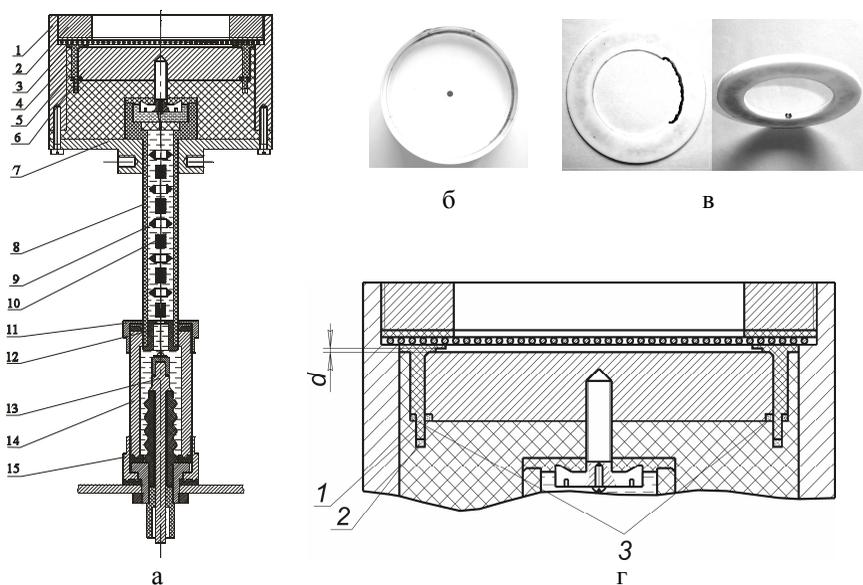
Схема конструкции: а - газоразрядного прибора (1 - корпус; 2 - анодное кольцо; 3 - анод-сетка с медным кольцом; 4 - изолятор катода; 5 - фторопластовая прокладка; 6 - катод; 7 - крышка корпуса; 8 - фторопластовая оболочка; 9 - стабилизирующие диски; 10 - трубочки; 11 – верхняя крышка высоковольтного ввода; 12 – фторопластовый стакан; 13 - керамический ввод; 14 – корпус высоковольтного ввода; 15 – нижняя крышка высоковольтного ввода); б, в - фотографии следов электропробоя на элементах катодного узла ВГП; г – схема катодного узла (1 - п-образная проточка; 2 - вакуумное масло; 3 - вакуумная резина)
